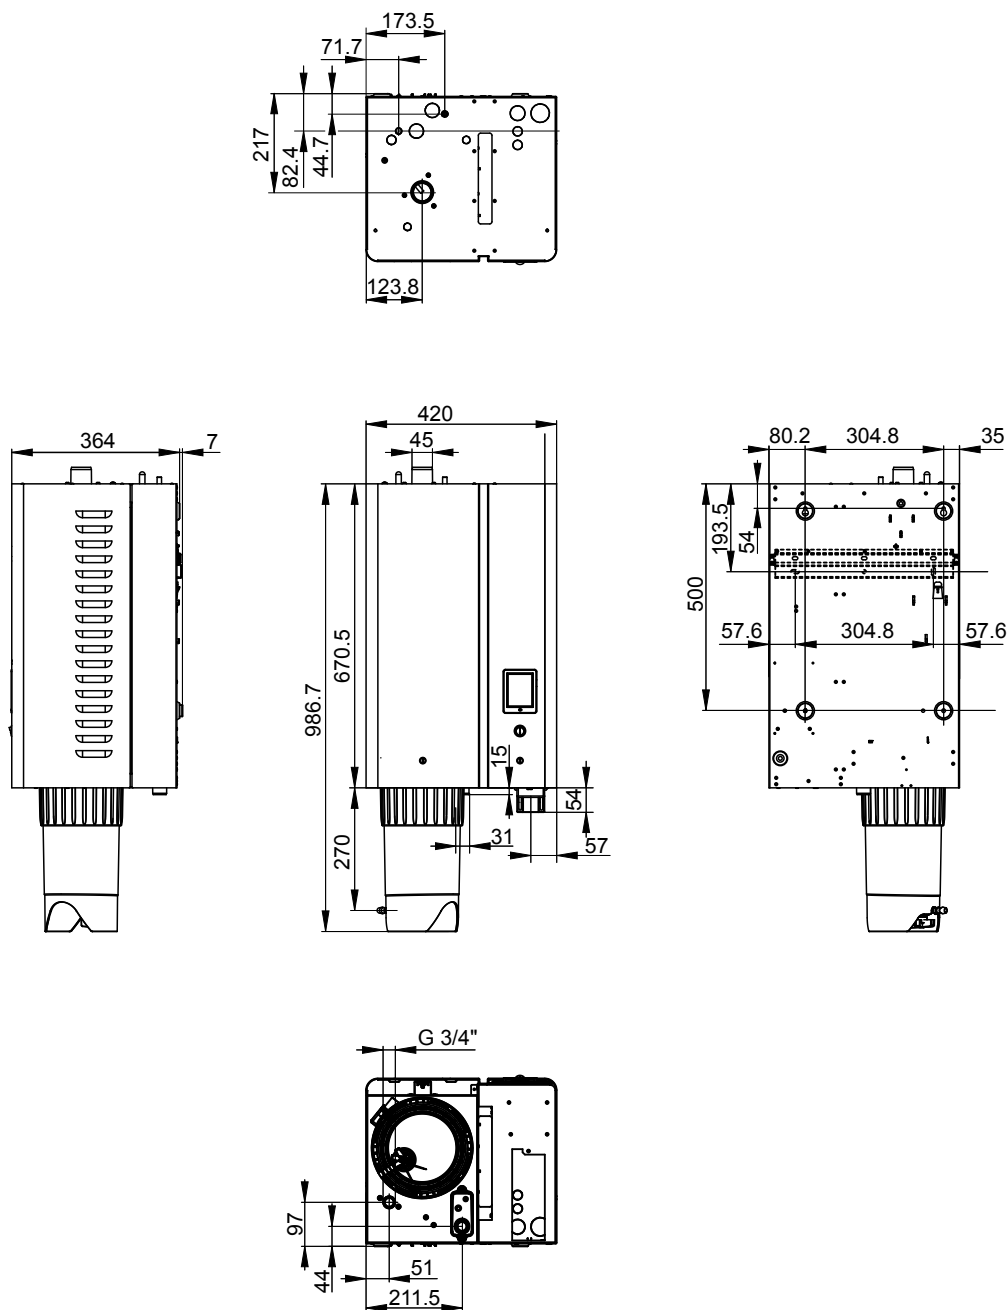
Чертеж с размерами устройства "S" (размеры в мм)
